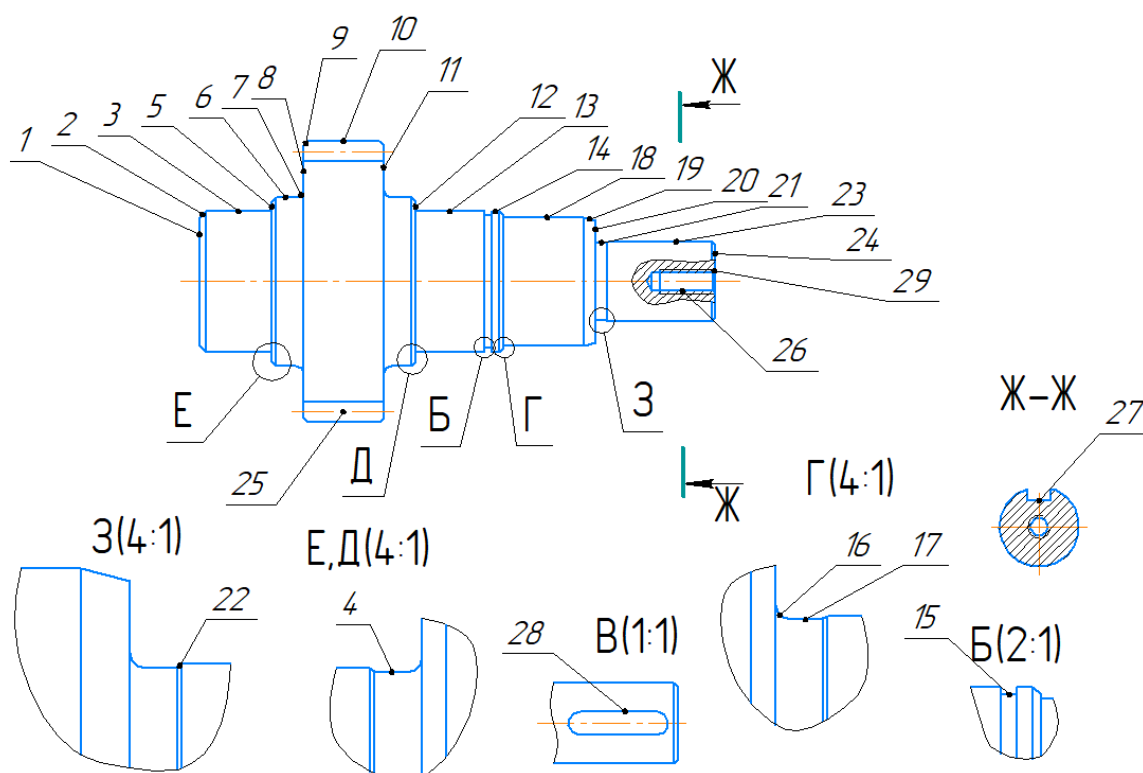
нумерація поверхонь вала-шестерні
